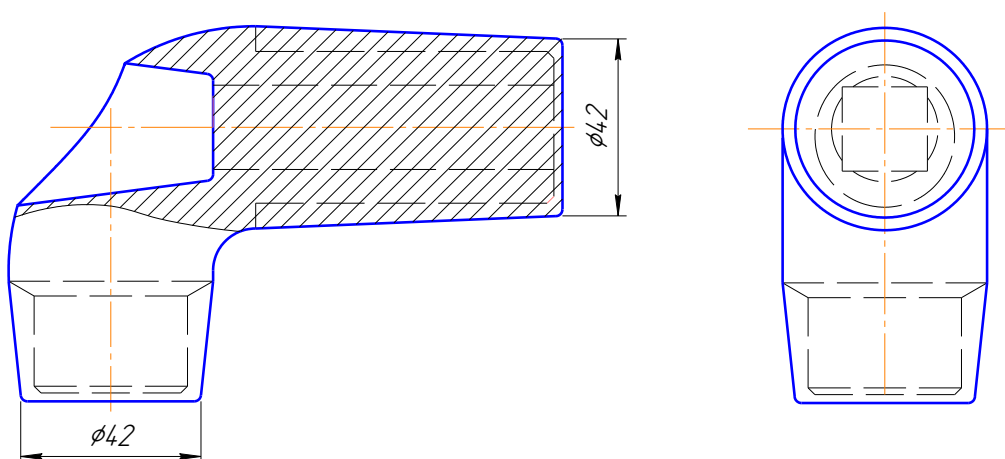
Конструкція заготовки деталі «Цапфа ричага».
